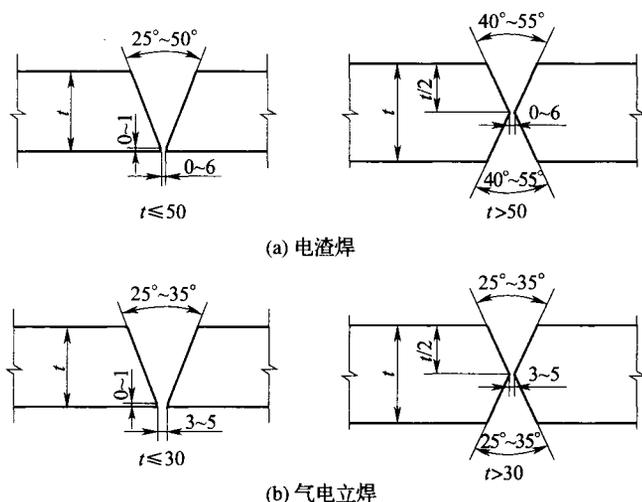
电渣焊和气电立焊缝坡口形式和尺寸
